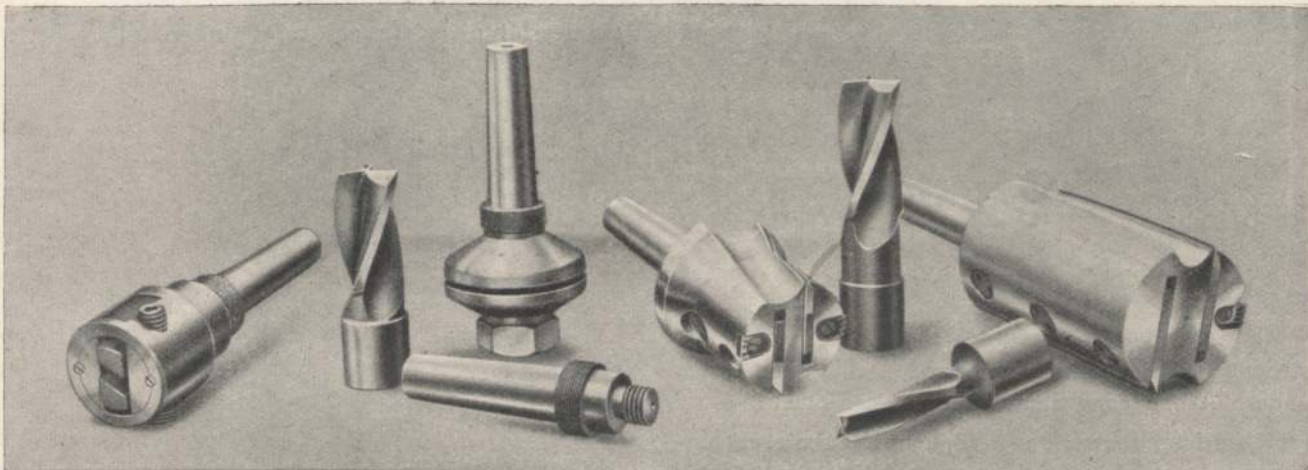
Werkzeug-Abbildungen, wie sie für die „Holz-Her“-Maschine verwendet werden. Mit den eigenartig konstruierten Fräsern können Zapfen bis zu 12 cm Länge gleichzeitig mit Zapfenfasen angefräst werden.
